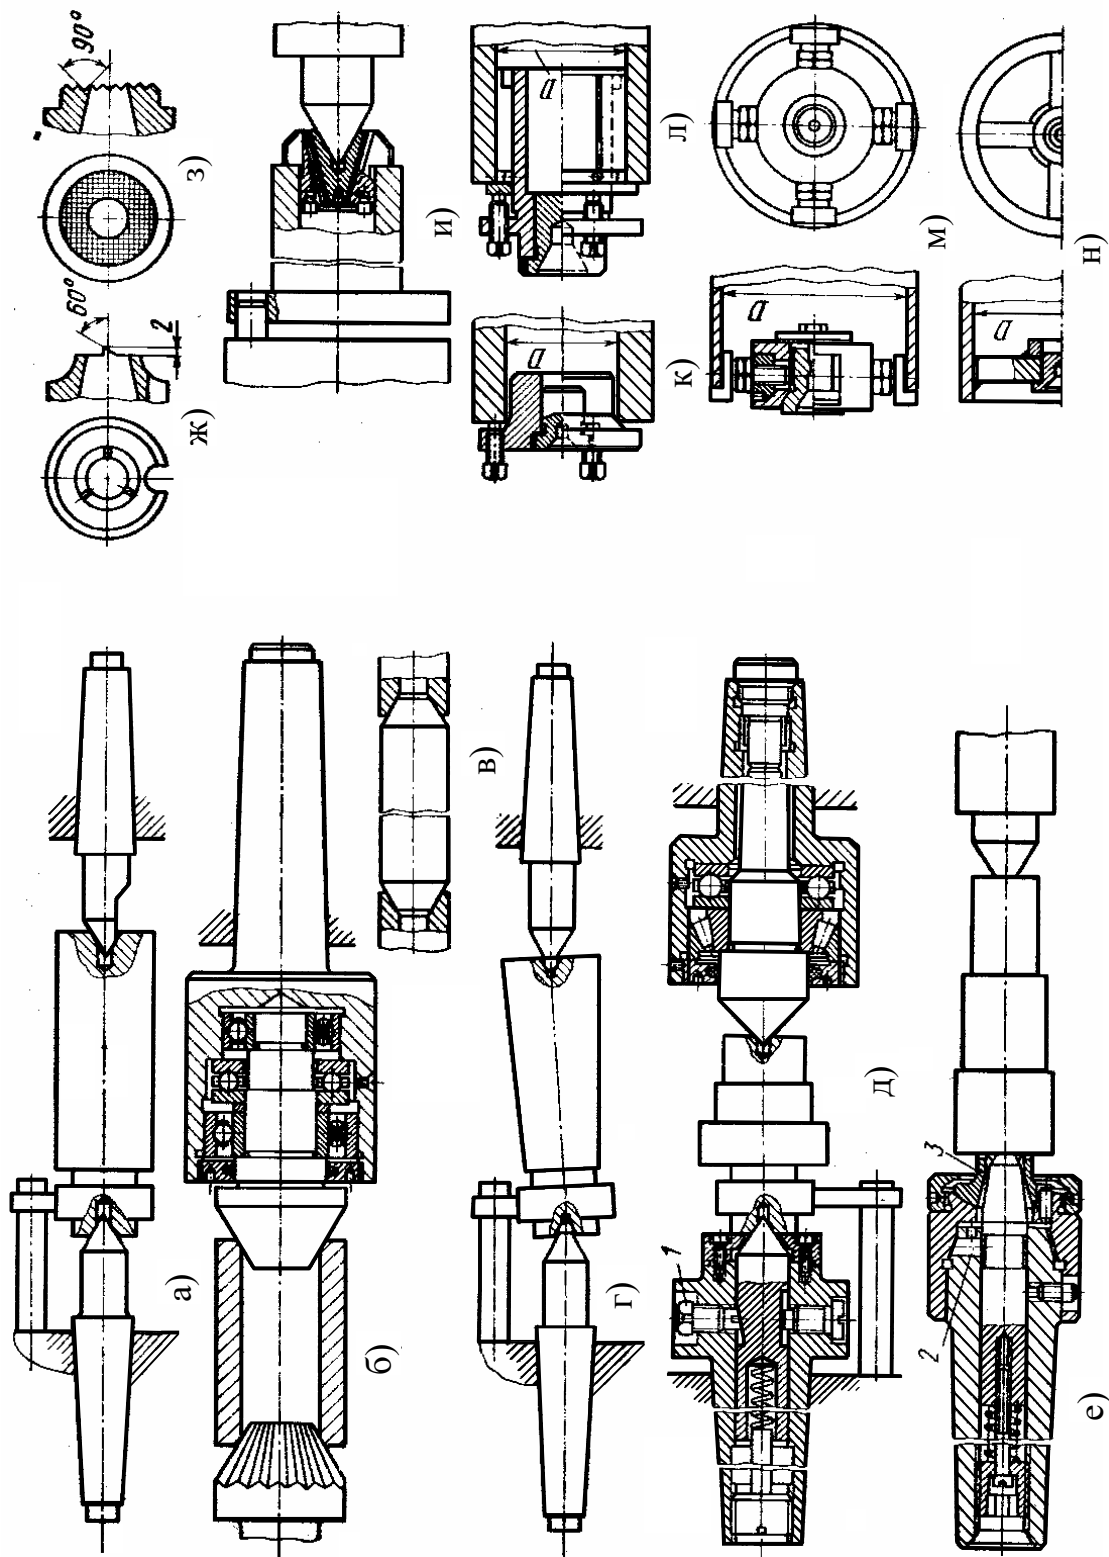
Схеми установлення заготовок на центрах токарних верстатів
